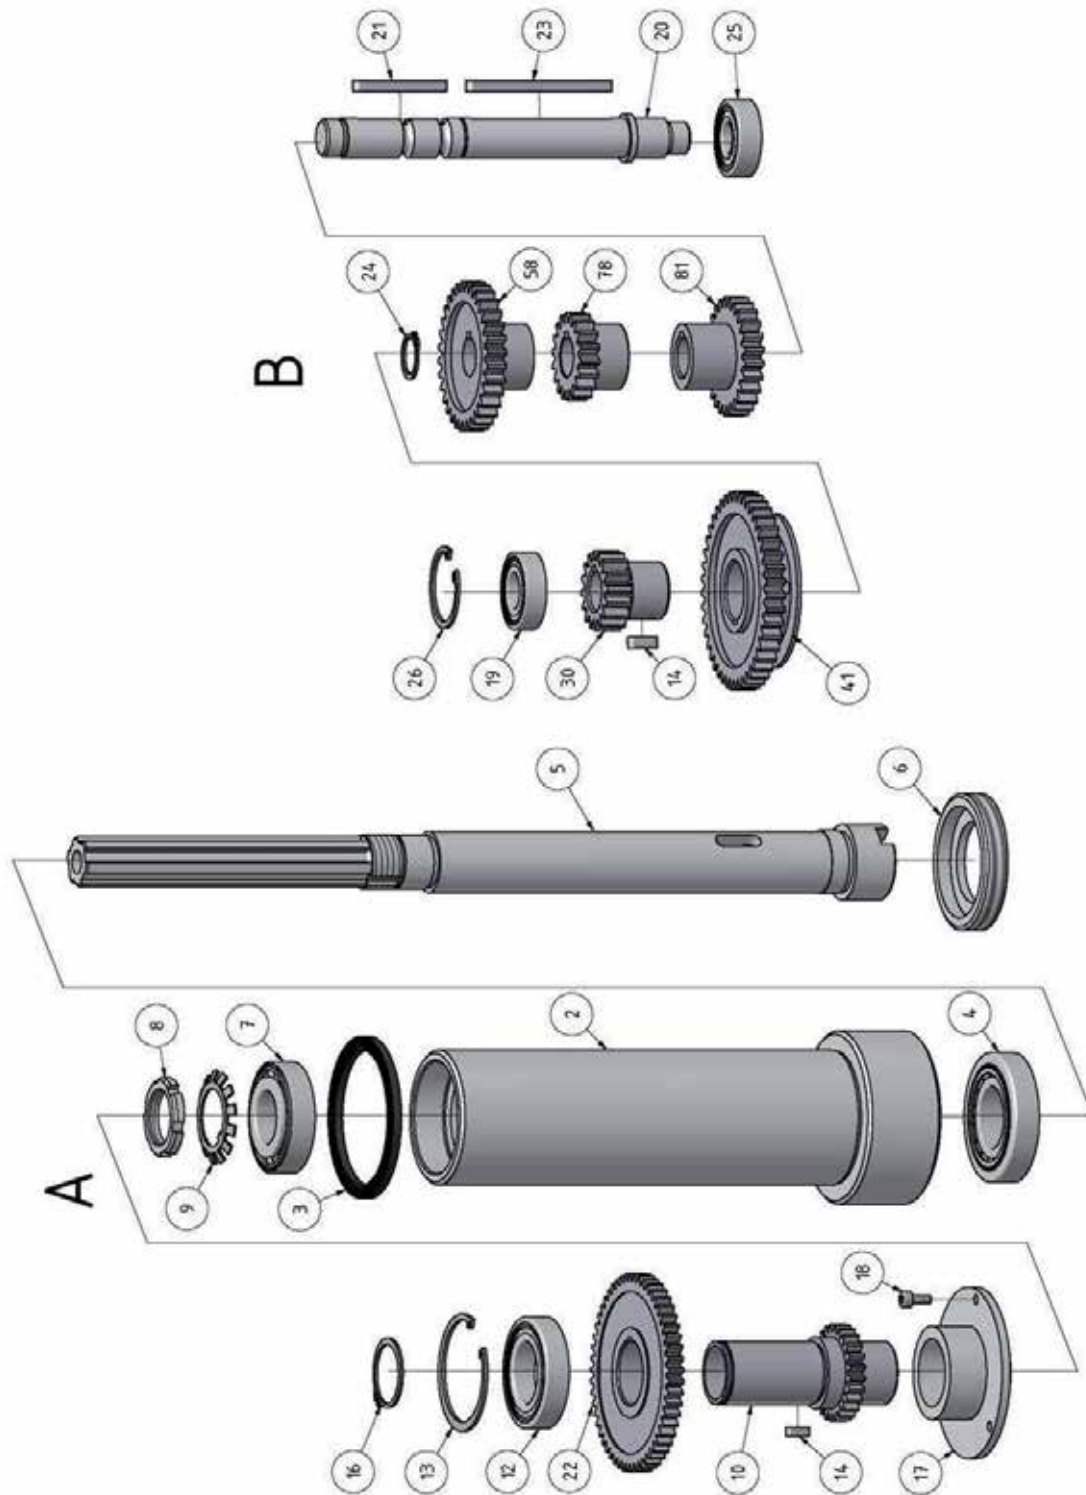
Bohrkopf 2 von 7 - Drilling head 2 von 7
